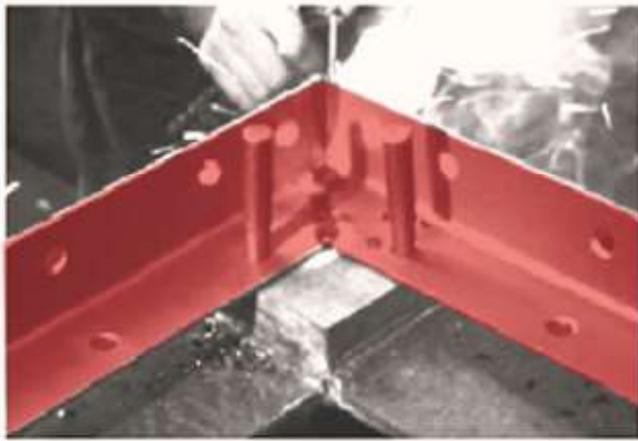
Unión de los perfiles en L mediante soldadura.
